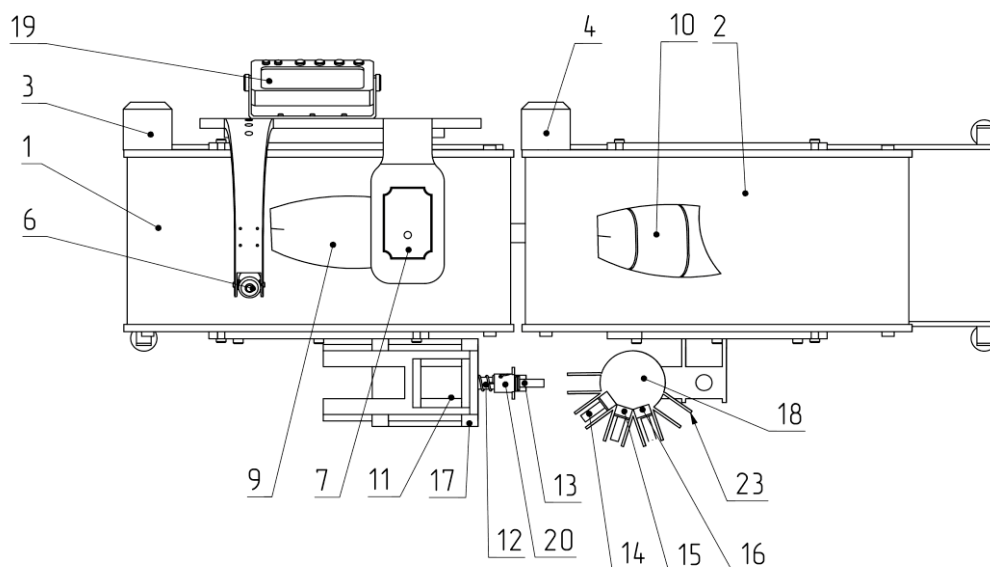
Устройство для резки рыбного филе (вид сверху)
